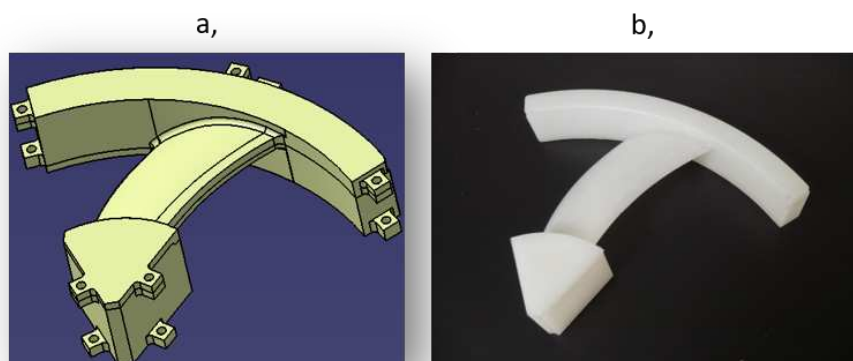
Réalisation d'un moule de 1/6 du ventilateur: (a) géométrie du moule (CAO), (b) pale obtenue par rotomoulage avec le moule considéré
